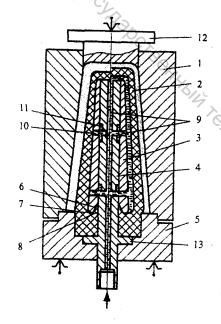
Схема устройства для формования изделий с глухим отверстием 1 - матрица; 2 - эластичная оболочка; 3 - вставка; 4 - стержень; 5 - основание; 6 - отверстие; 7 - торец, 8 - поверхность свободная; 9 -, 10, 11 - каналы; 12 - упор; 13 - опора (ступень)
